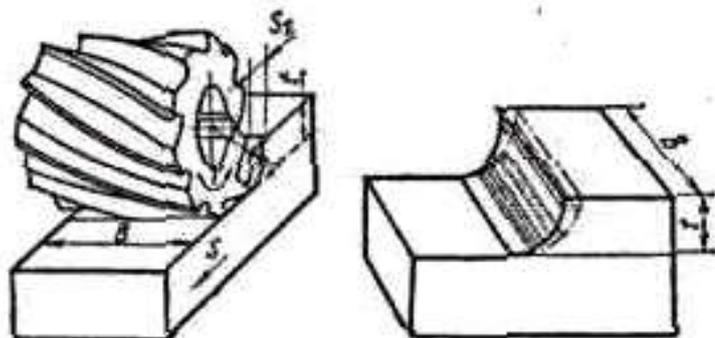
Фрезерование цилиндрической винтовой фрезой: B — ширина фрезерования, t — глубина фрезерования, s — наибольшая толщина среза
